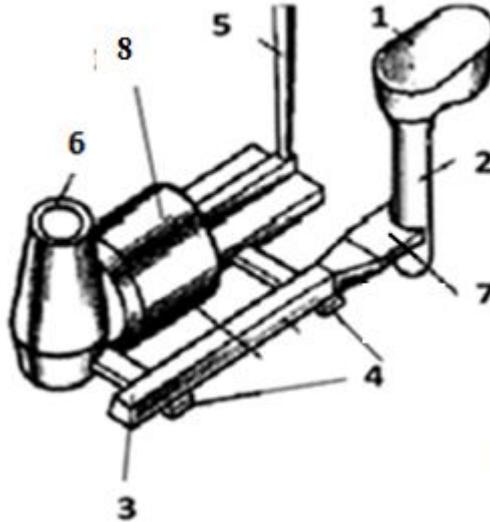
Элементы литниковой системы: 1 – литниковая воронка (чаша); 2 – стояк; 3 – шлакоуловитель; 4 – питатели (литники); 5 – выпор; 6 – прибыль; 7 – дроссель; 8 – отливка
